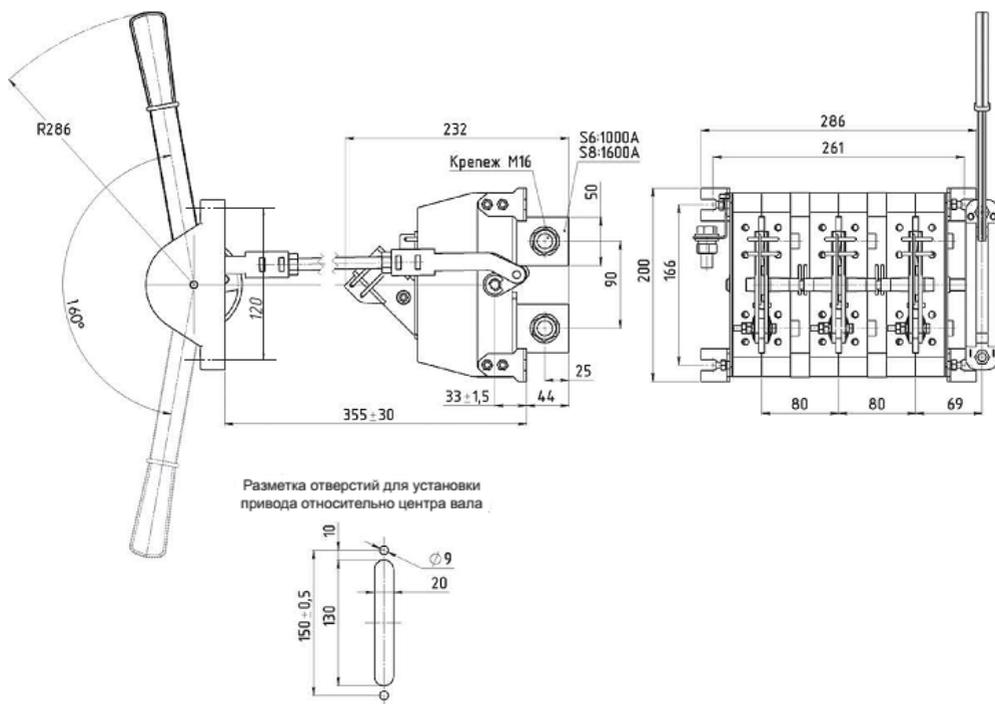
Разъединитель PE19-41(43)-31150-00 УХЛЗ с боковой смещенной рукояткой
